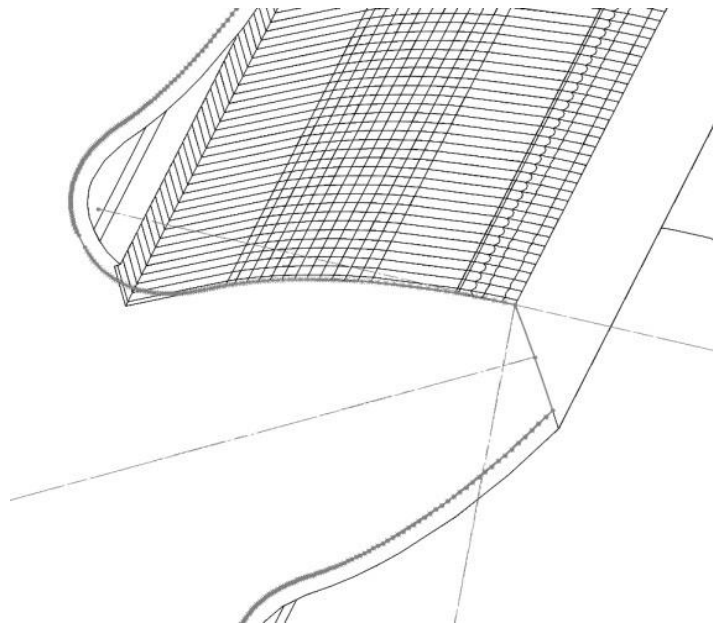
Схема формоутворення сітки на оброблюваній поверхні зубчастого колеса
